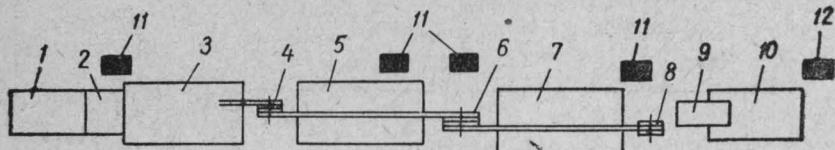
Схема расположения частей агрегата МТ-530-Л:
